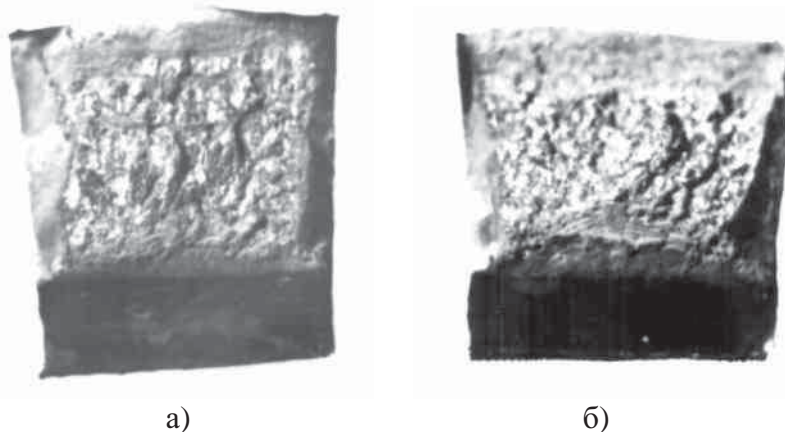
Поверхность излома ударных образцов с V-образным надрезом посередине металла шва: $\times 5,5$. а) – автоматическая сварка по штатной технологии; б) – по предлагаемой
